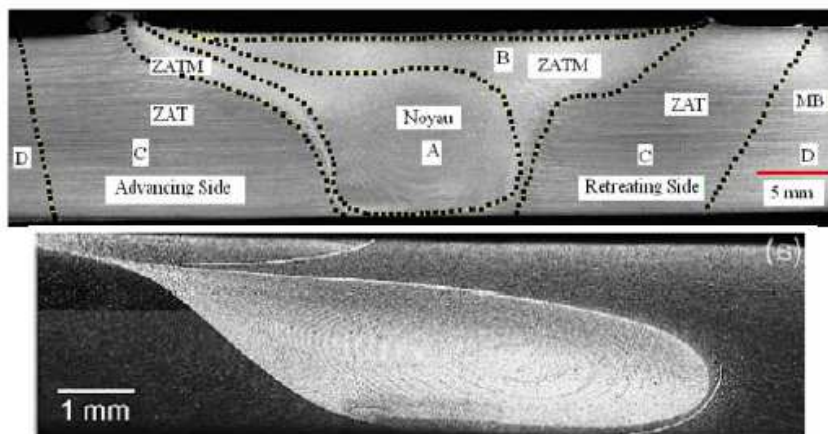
Profil d'un joint soudé par FSW [18].
